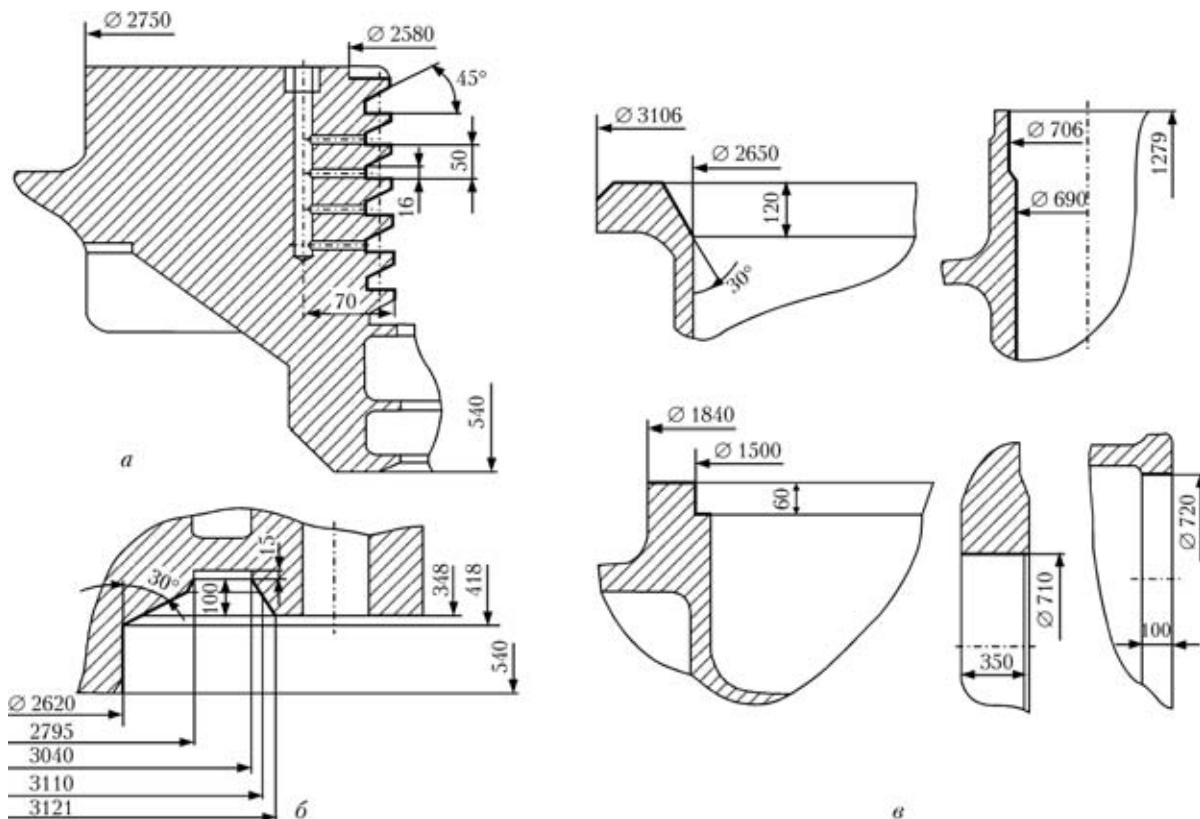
Наплавляемые поверхности (жирные линии) корпуса кольца (а, б) и станины конусной дробилки (в)
